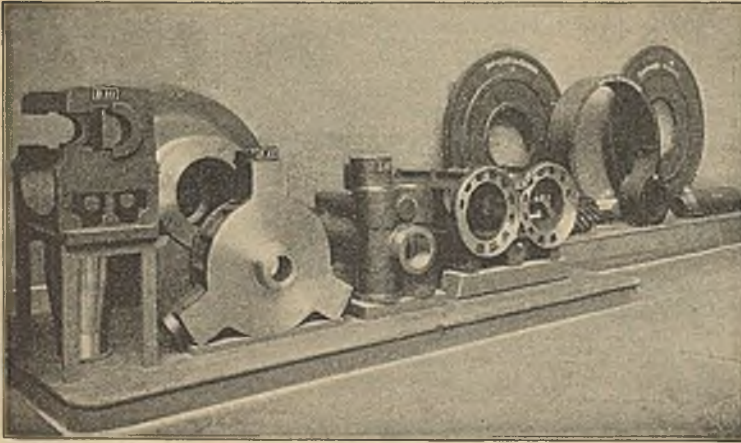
Pivotgabel, Rahmen für Dreizylinder-Maschine, Pumpenzylinder, Rahmen für eine Dampfmaschine, Kollergangsteile, Lagerrolle.
